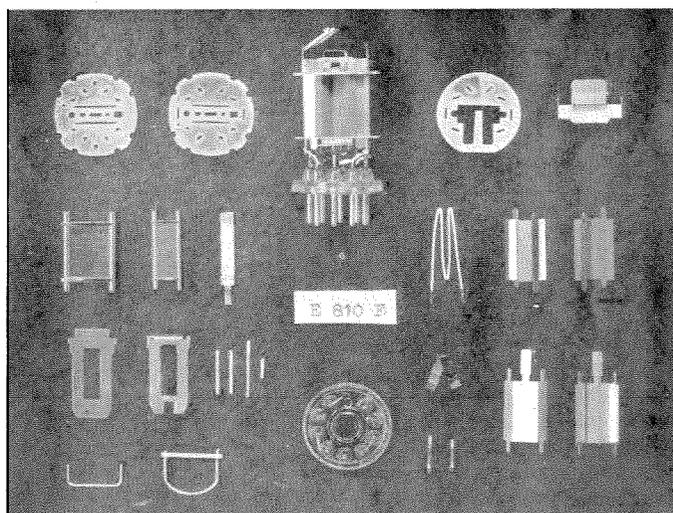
Vue des pièces d'un tube S.Q., le tube E 810 F.
